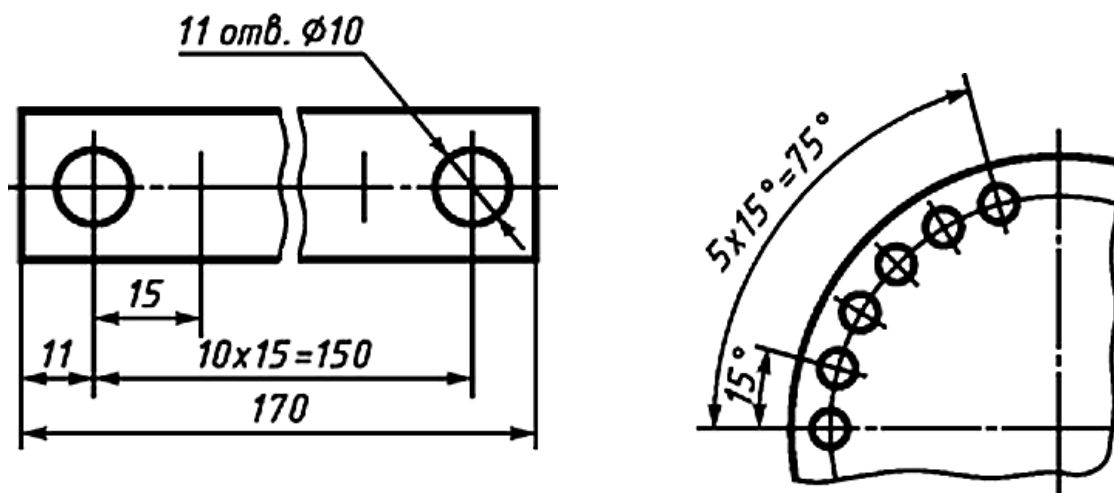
Размеры равномерно расположенных одинаковых элементов
